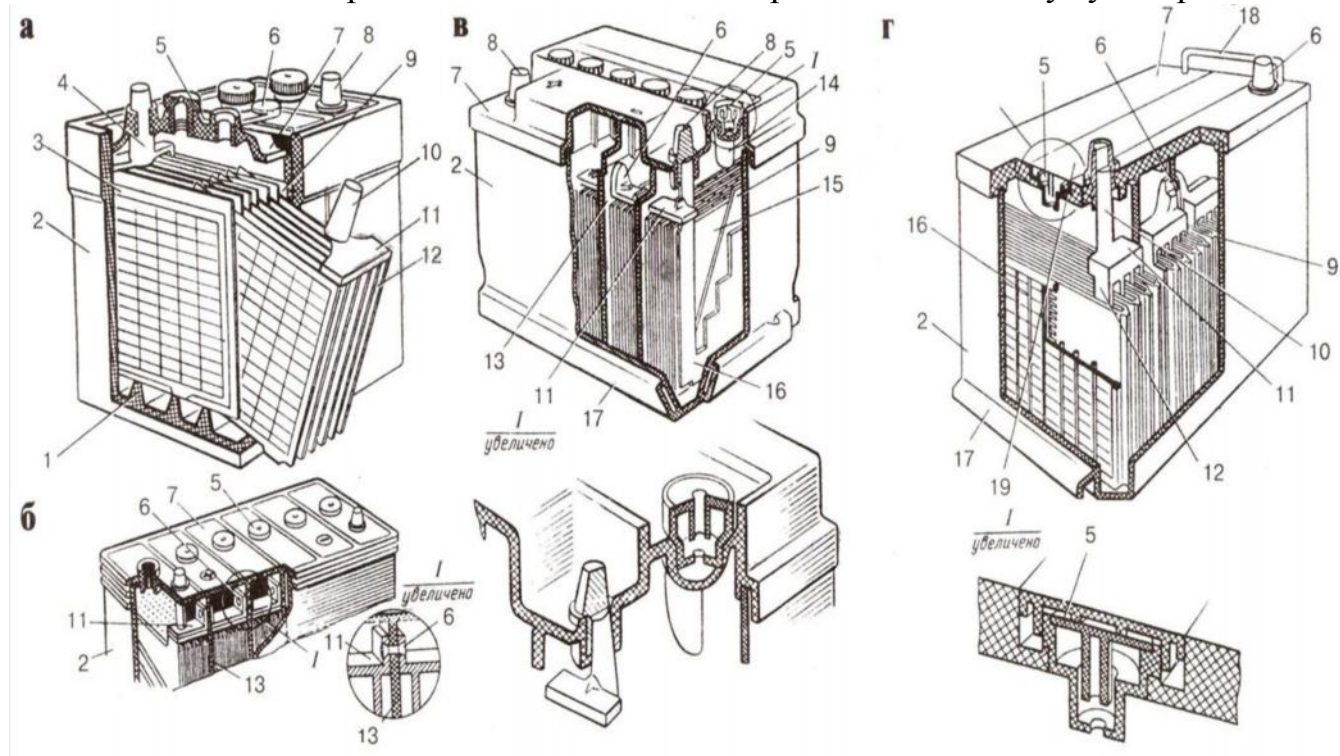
Аккумуляторные батареи: а- в моноблоке с ячеечными и межэлементными перемычками над крышками; б, в, г - с межэлементными перемычками через перегородки; 1 - опорные призмы моноблока; 2- моноблок; 3 - полублок отрицательных электродов; 4 - баретка; 5 - пробка; 6- межэлементная перемычка; 7- крышка; 8 - полюсный вывод; 9 - сепаратор; 10 - борн; 11 - мостик; 12
